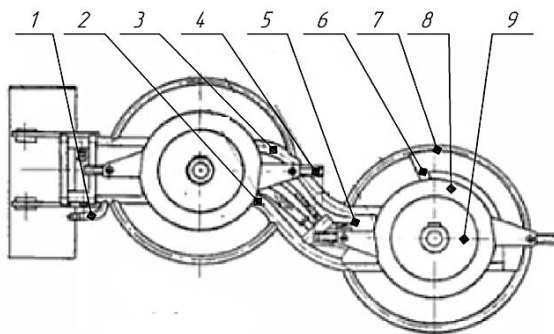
Режущий аппарат косилки К-24АМ: 1, 2 и 3 – маслопроводы; 4 – ножи; 5 – корпус; 6 – роторы; 7 – тарельчатые опоры; 8 – крестовина; 9 – колпак
